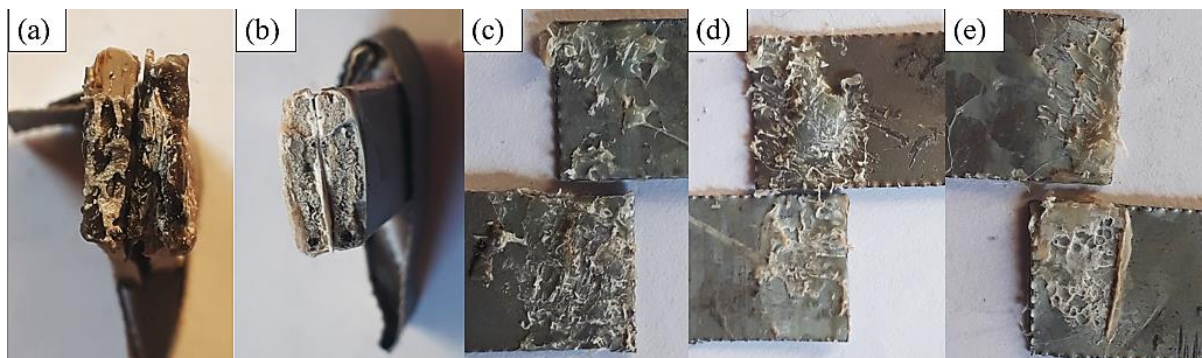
Rupture cohésive des éprouvette assemblé par acrylique modifié (a) PE (b) PVC (c) acier inox (d) acier galvanisé (e) aluminium.
